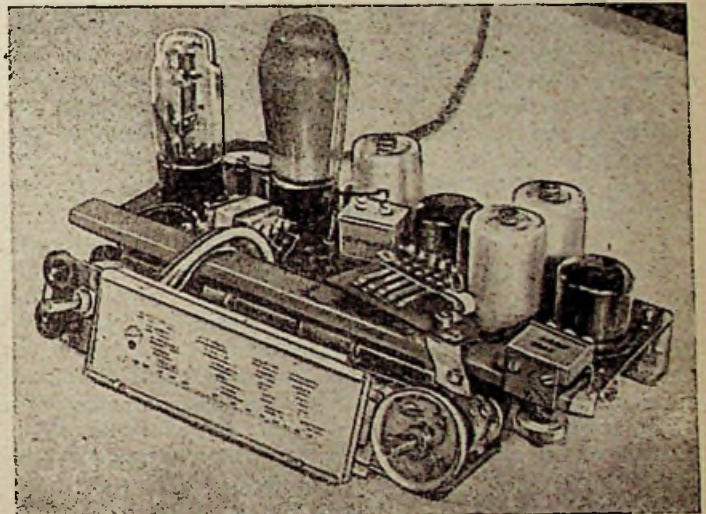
Chassis des Blaupunkt-Super 4 GW 647 K. Aufgebaut ist das Gerät ähnlich wie der 4 GW 646. Es sind für diesen Apparat jedoch ein sechster Kreis, Kurzwellenteil, Feinantrieb und beleuchtete Skala vorgesehen. Aufnahme: Kunst und Technik
